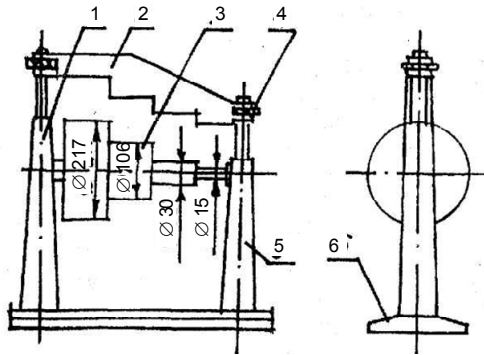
Пристрій для визначення гнучкості: 1 — опора; 2 — притискна планка; 3 — циліндр; 4 — гайка; 5 — опора; 6 — основа
